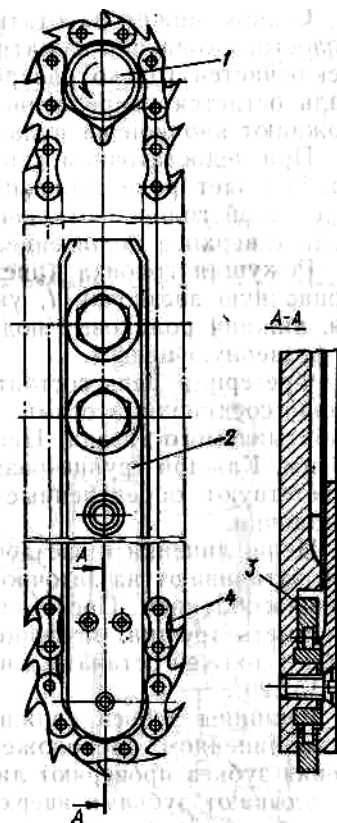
Режущая головка цепнодолбежного станка ДЦА-4:
